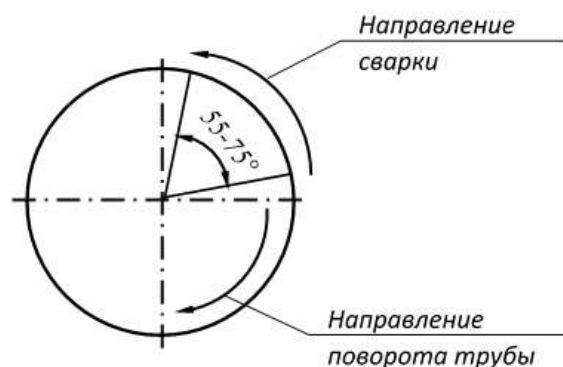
Схема сварки стыка труб малого диаметра.
